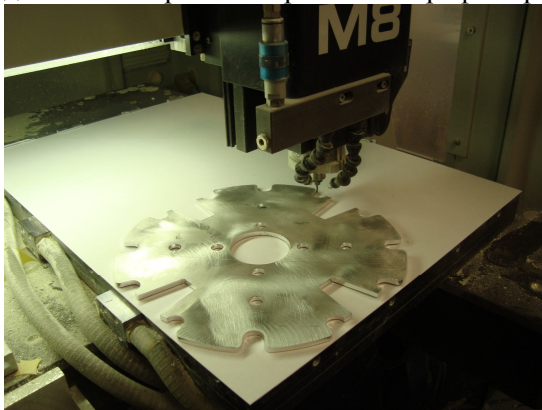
Процес фрезерування криволінійної поверхні привідної зірочки трубчатого конвеєра
